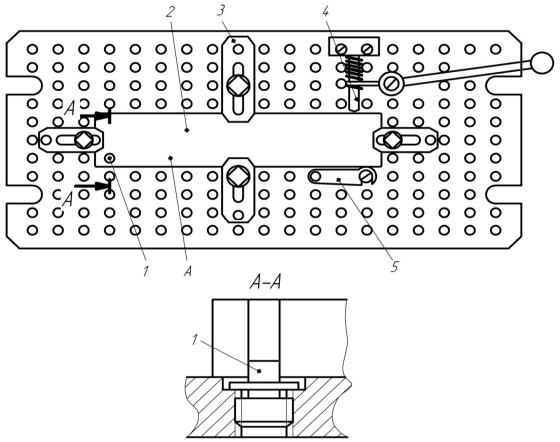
Модульное приспособление для установки плоской детали: 1 — штырь; 2 — заготовка; 3 — прихват; 4 — прижим горизонтальный с рукояткой; 5 — защелка
